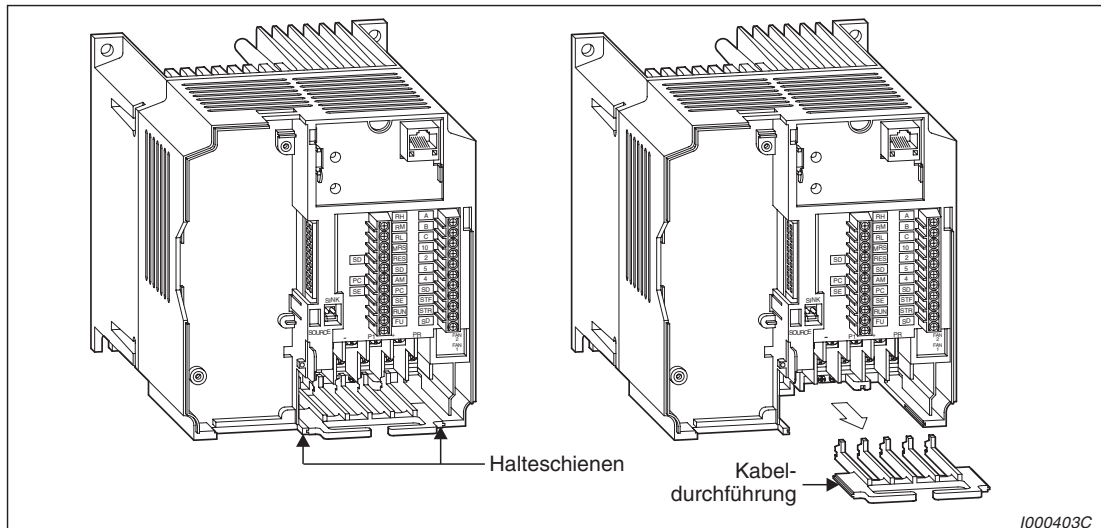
Aus- und Einbau der Kabeldurchführung
